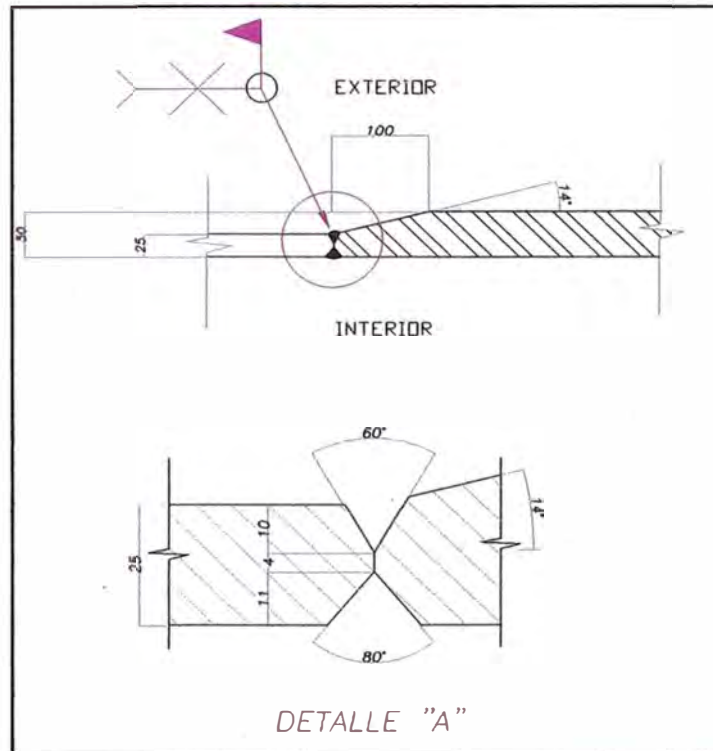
JUNTA ENTRE PLANCHAS DE 25 MM Y 50 MM
